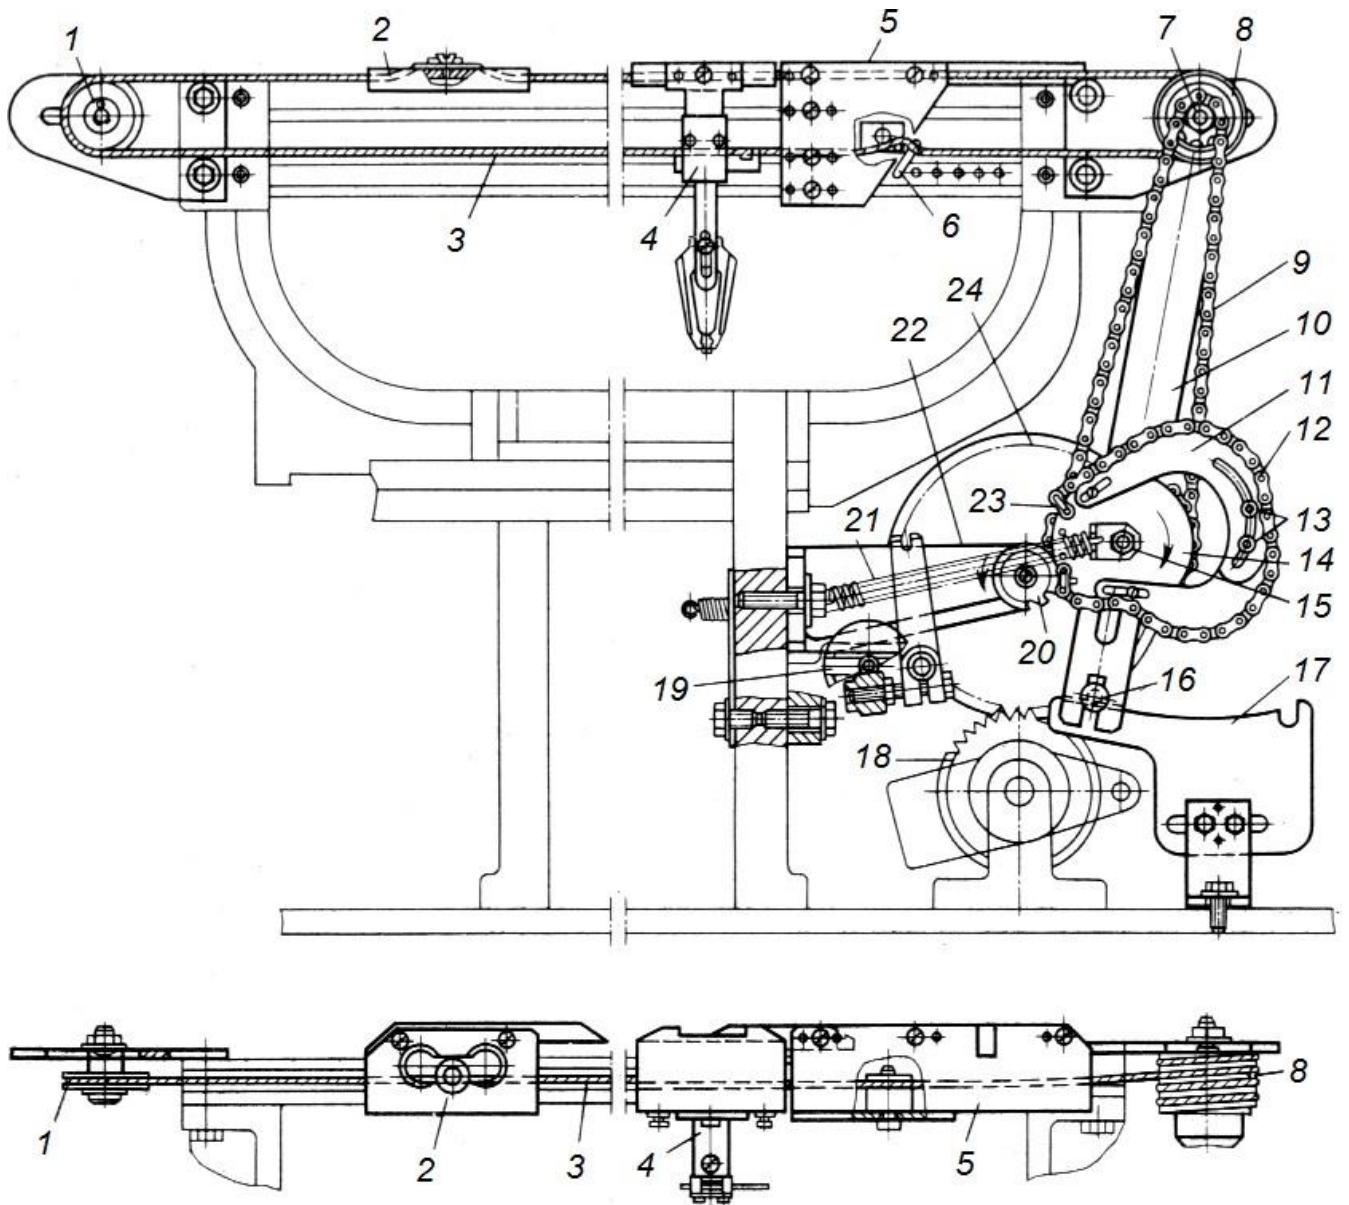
Конструктивна схема механізму зменшення ширини в'язання машини-напівавтомата ПВК.
